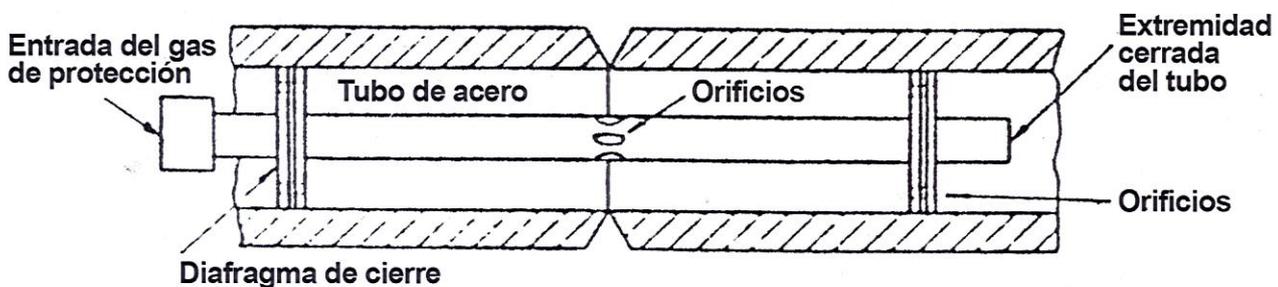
| Protección de gas en el interior de un tubo para soldadura TIG.
